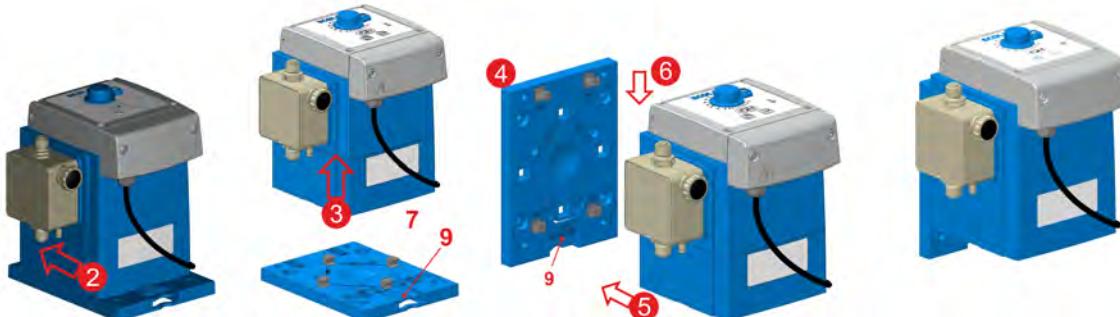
Passage du montage sur table (debout) au montage mural (suspendu)
